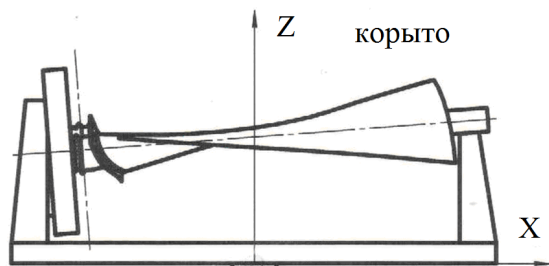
Установка в приспособлении заготовки на станке с ЧПУ ФП-17
